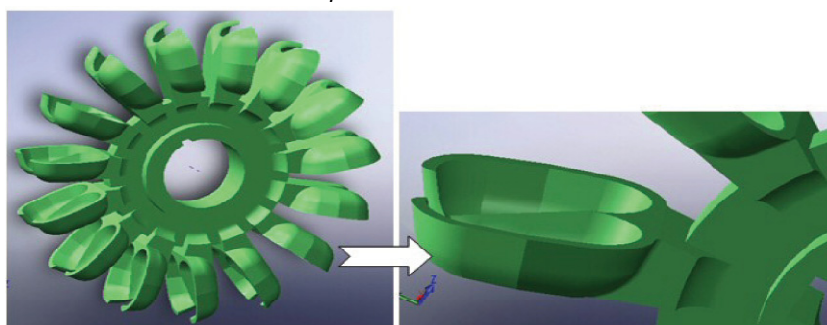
Studiul de caz 1. Palete de turbină monobloc cu butucul rotorului Pelton [27]
